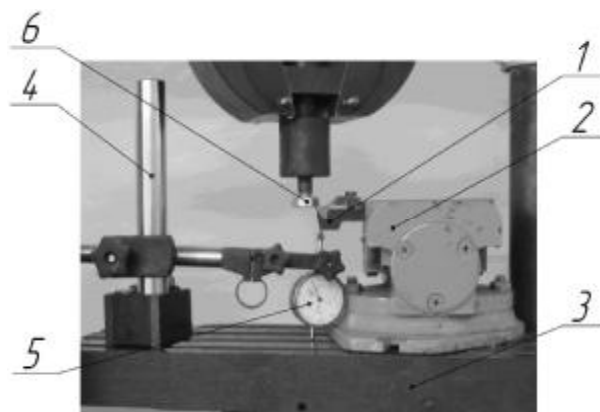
Загальний вид установки для вимірювання переміщень голівки відрізного різця з бічною установкою БНП: 1 – відрізняльний різець; 2 – лещата; 3 – стіл; 4 – магнітна стійка; 5 – індикатор годинникового типу; 6 – натискний елемент
